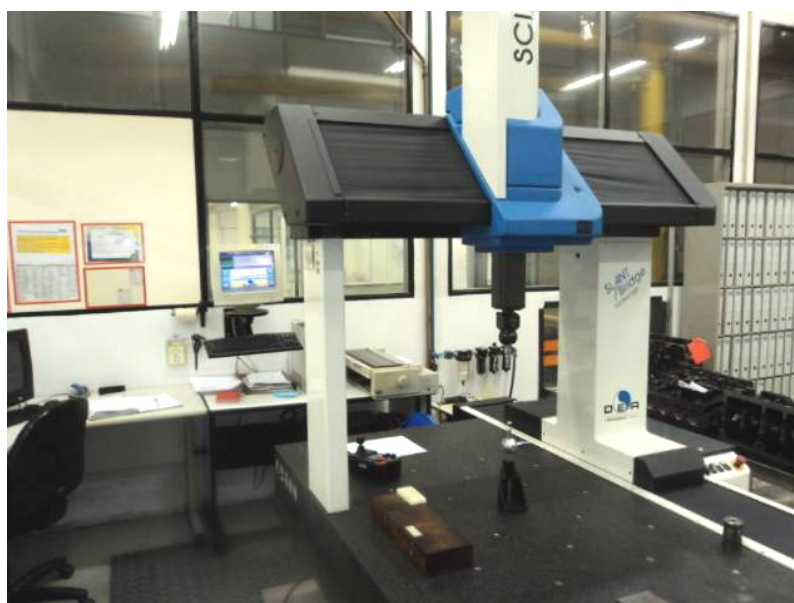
Máquina de Medição Tridimensional marca DEA Scirocco.
